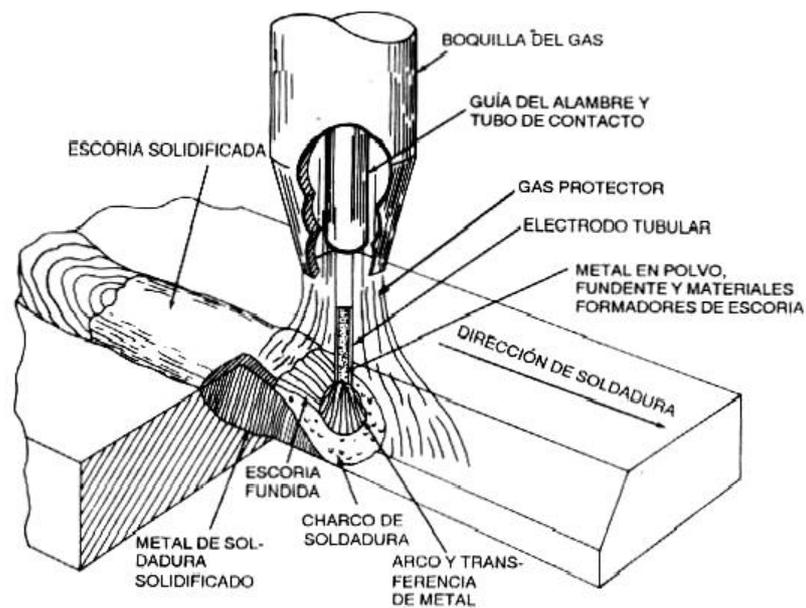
Esquema de la soldadura por arco con núcleo de fundente.
